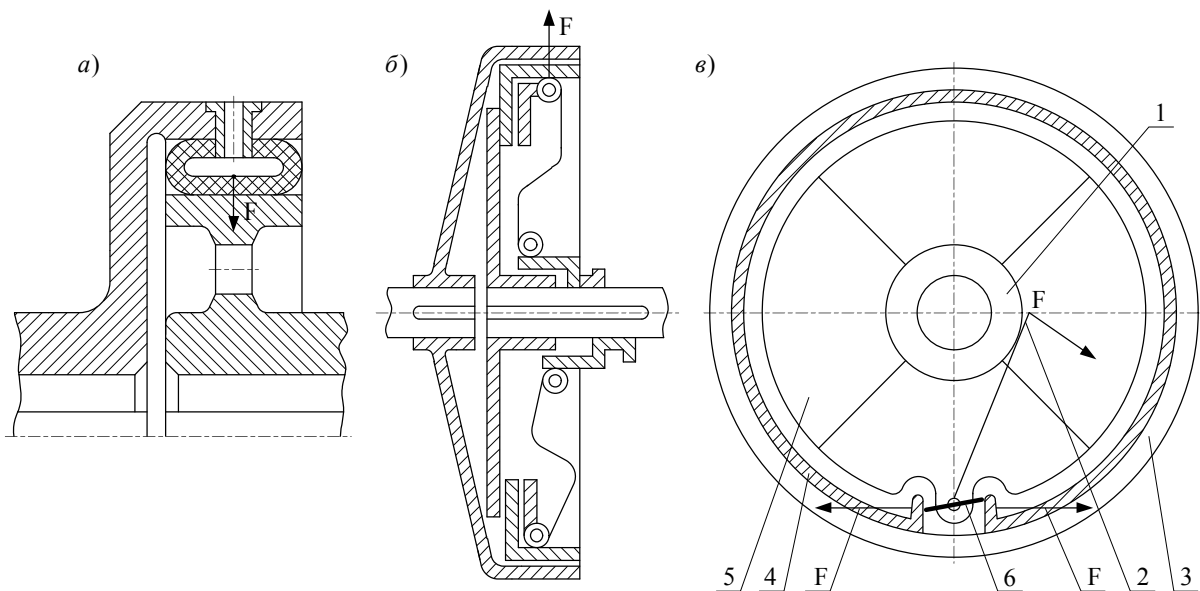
Схеми муфт з циліндричними поверхнями тертя
